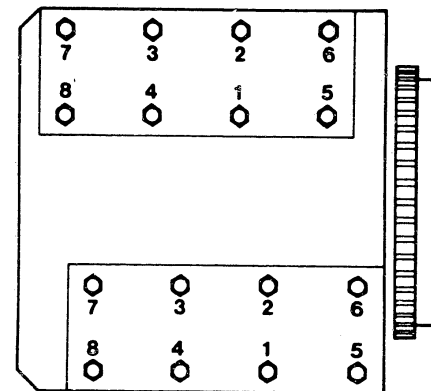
Motor Z7V: Anzugsreihenfolge der beiden Zylinderköpfe.
